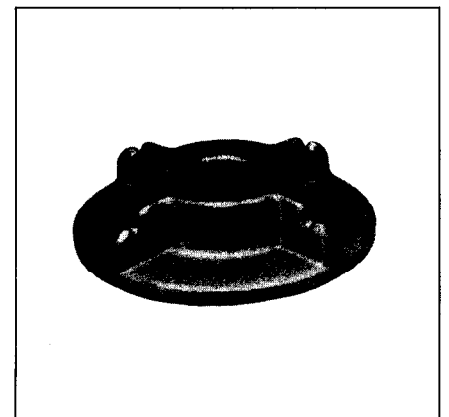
Druckteller (0,9 kg) für eine federnde Aufhängung von Siederohren im Kesselbau aus St 37-2
